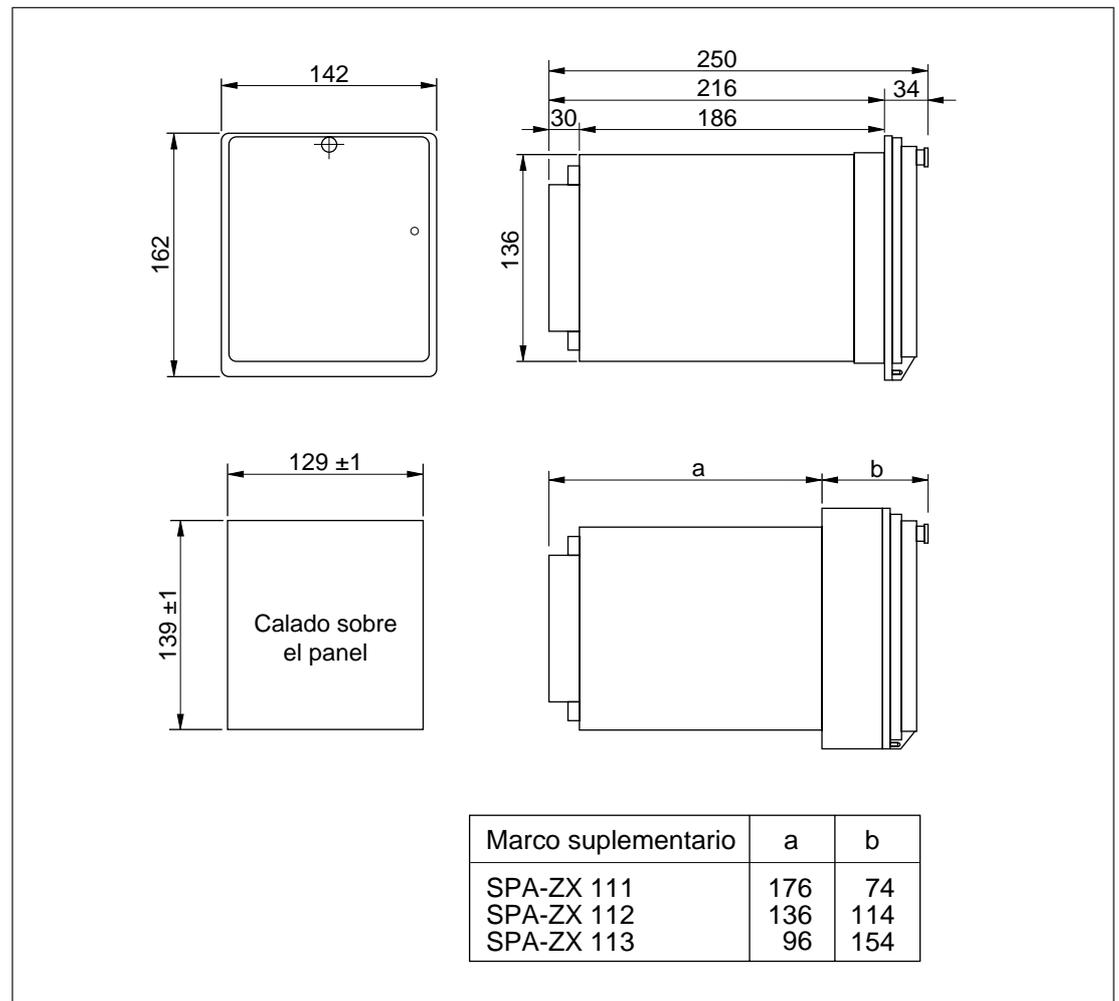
Dimensiones del relé de sobretensión residual SPAU 110 C
